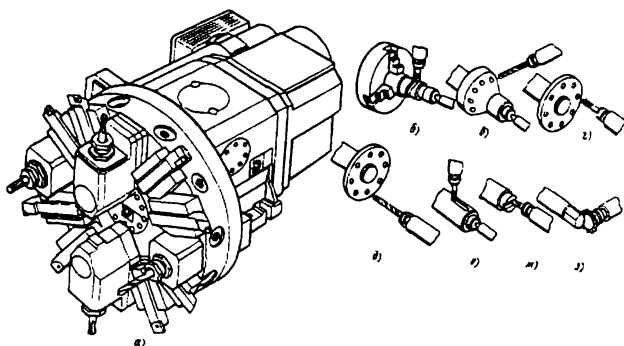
Револьверна головка з комплектом обертальних інструментів:
